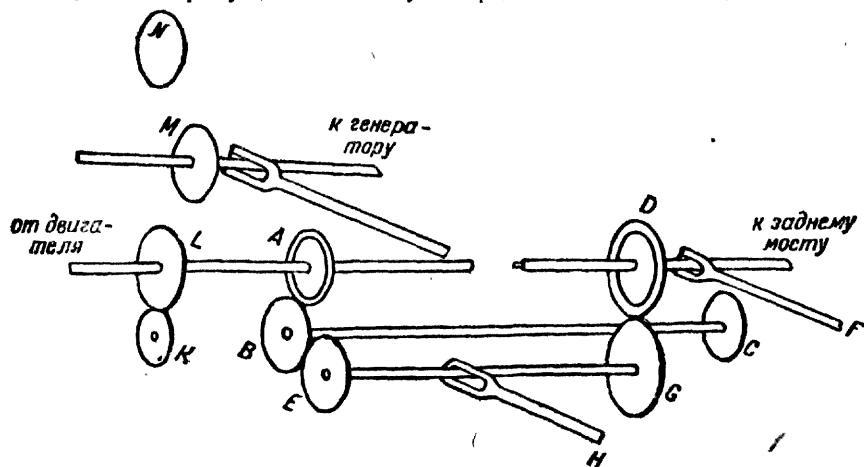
Кинематическая схема редуктора ПО-15-8.
